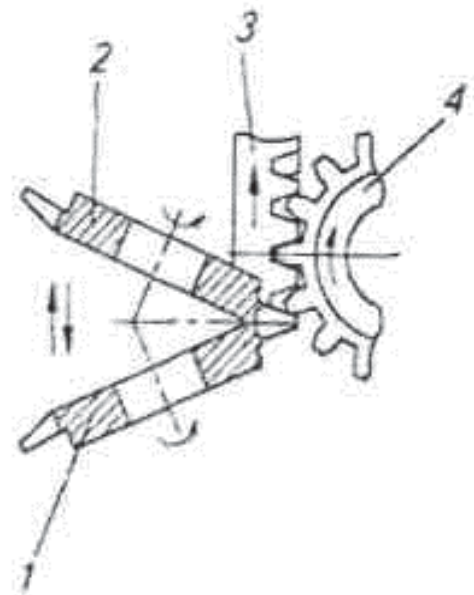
Схема нарезания зубьев парой фрез:
